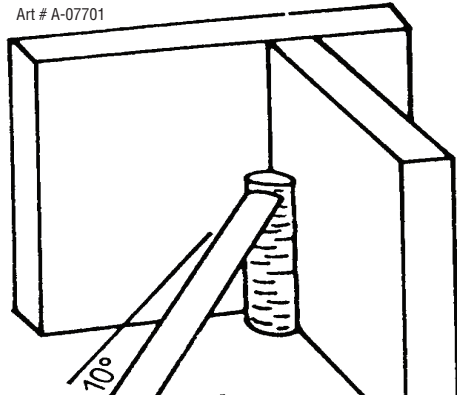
Soudure d'angle Verticale à un seul passage
